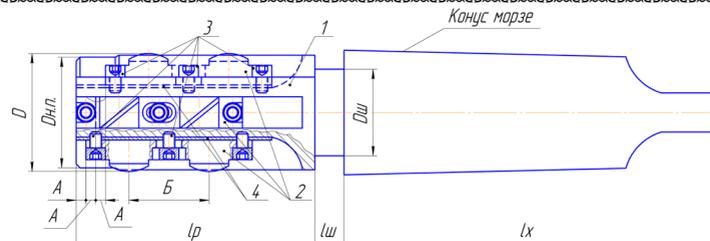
Общий вид сборной развёртки со двоянными безвершинными зубьями
